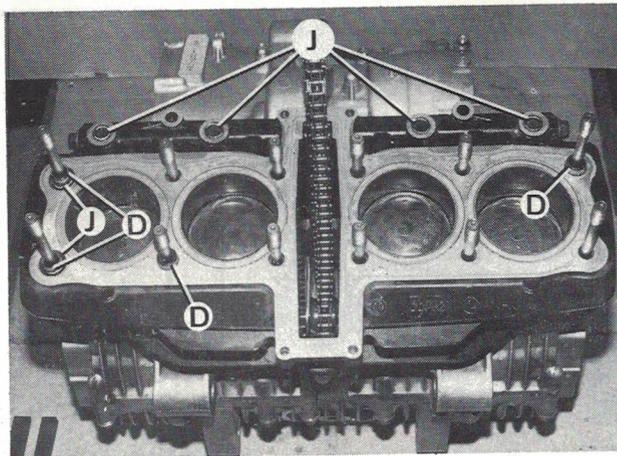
D. Douilles - J. Joints toriques (Photo RMT)
